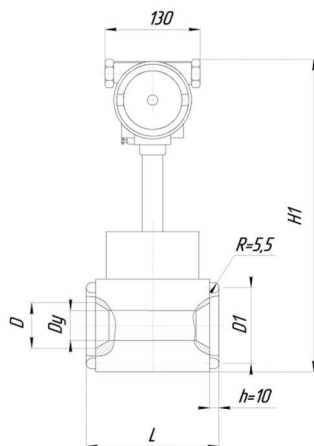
Габаритные и присоединительные размеры преобразователя расхода ТИРЭС на высокое давление (до 32МПа) (исполнение К);
